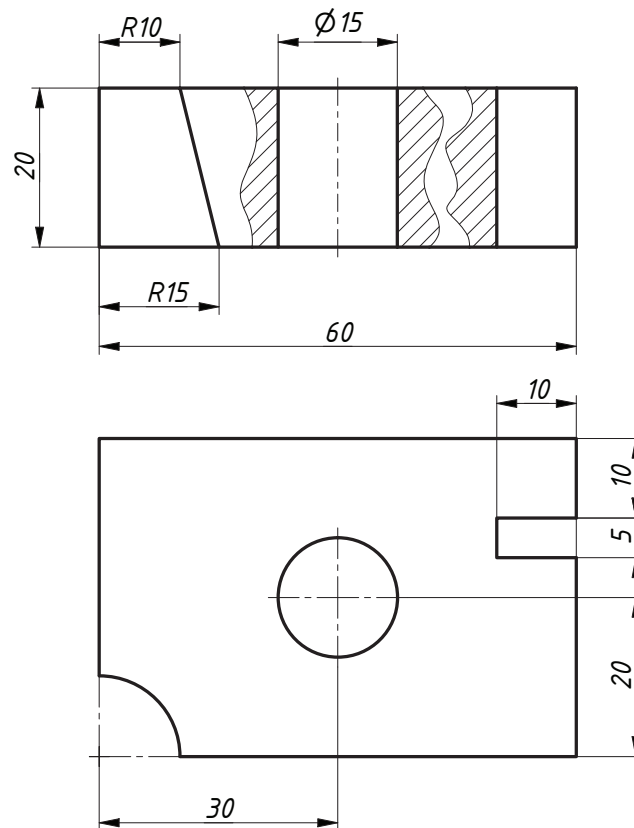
Фрагмент чертежа изделия с размерами, обеспечивающими определение каждого элемента детали
